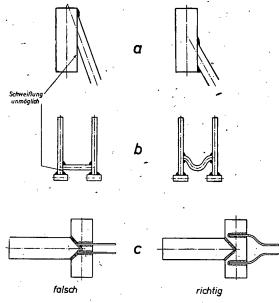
Schweißgerechte Gestaltung von Rohrverbindungen im Fahrzeugbau
